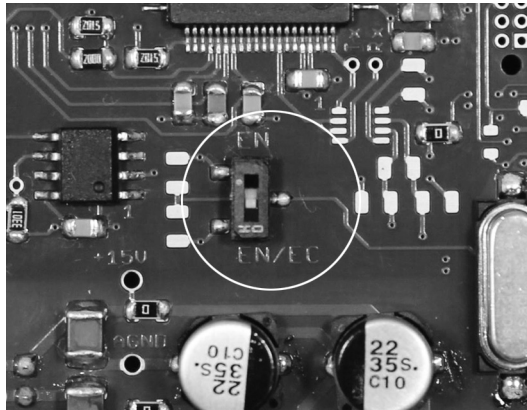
Wechsel zwischen Ethernet/EtherCAT, Grundmodul KSS6420
